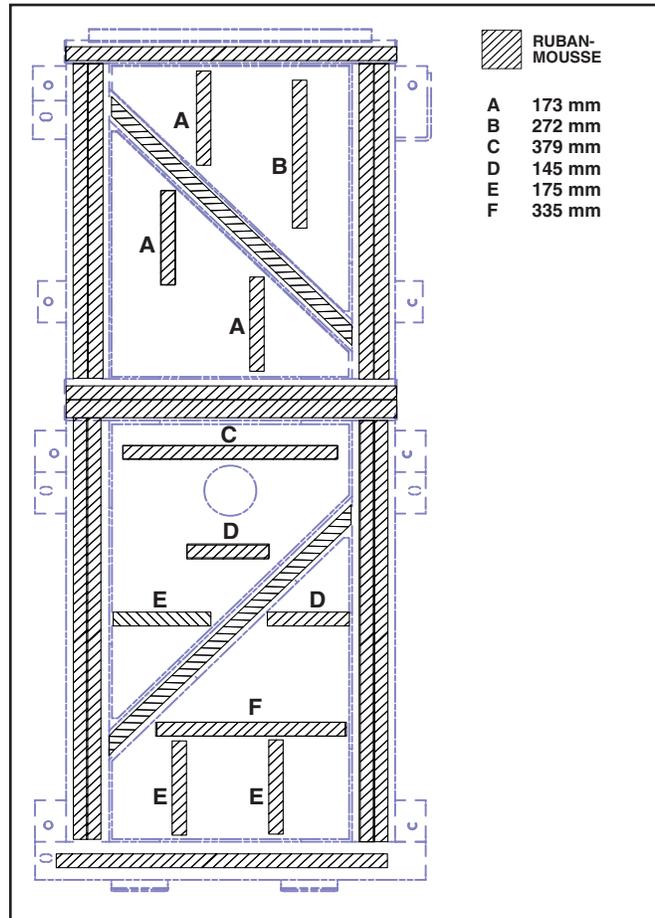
Pose de ruban-mousse sur berceau et panneaux
